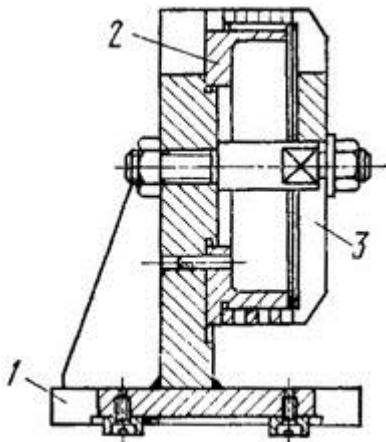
Фрезерное приспособление для разрезания поршневых колец:
